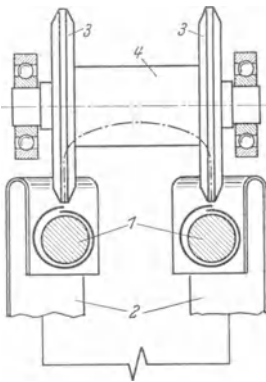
Doppelschlepprolle z. B. für Zinkbeckerschweißung. Den beiden Dornen 1 wird der Strom durch die Bänder 2 zugeführt. Die Elektrodenrollen 3 sind durch die Welle 4 kurzgeschlossen und laufen ganz leicht in Kugeln. Beide Nähte werden gleichzeitig geschweißt.
